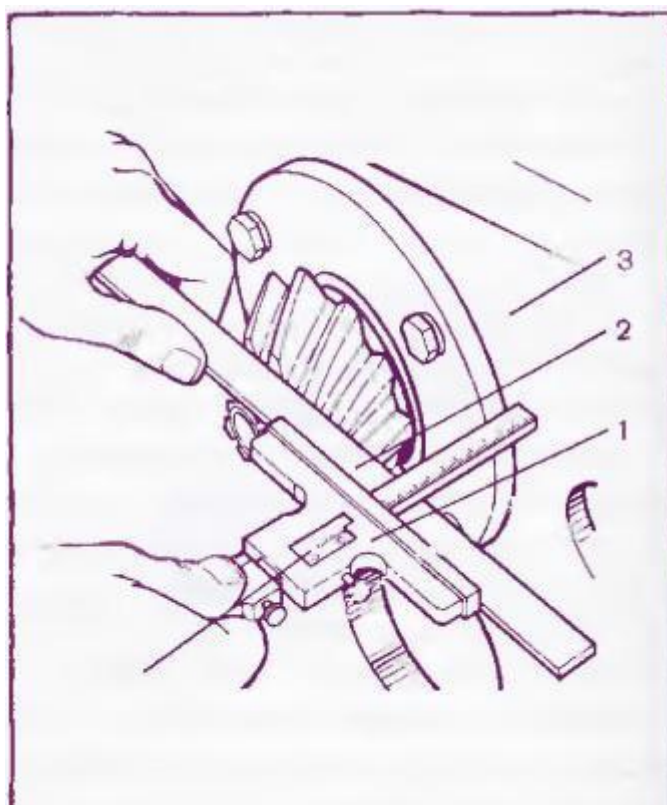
Проверка установочной высоты ведущей шестерни главной передачи МТЗ.
